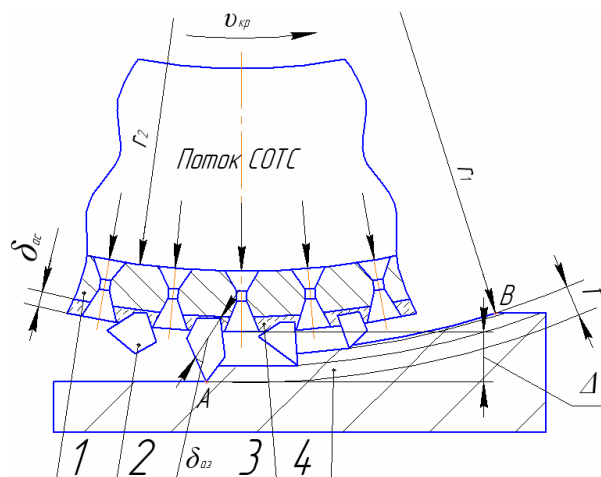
Схема работы алмазного круга: 1 – корпус круга; 2 – алмазное зерно; 3 – связка; 4 – обрабатываемая поверхность детали
